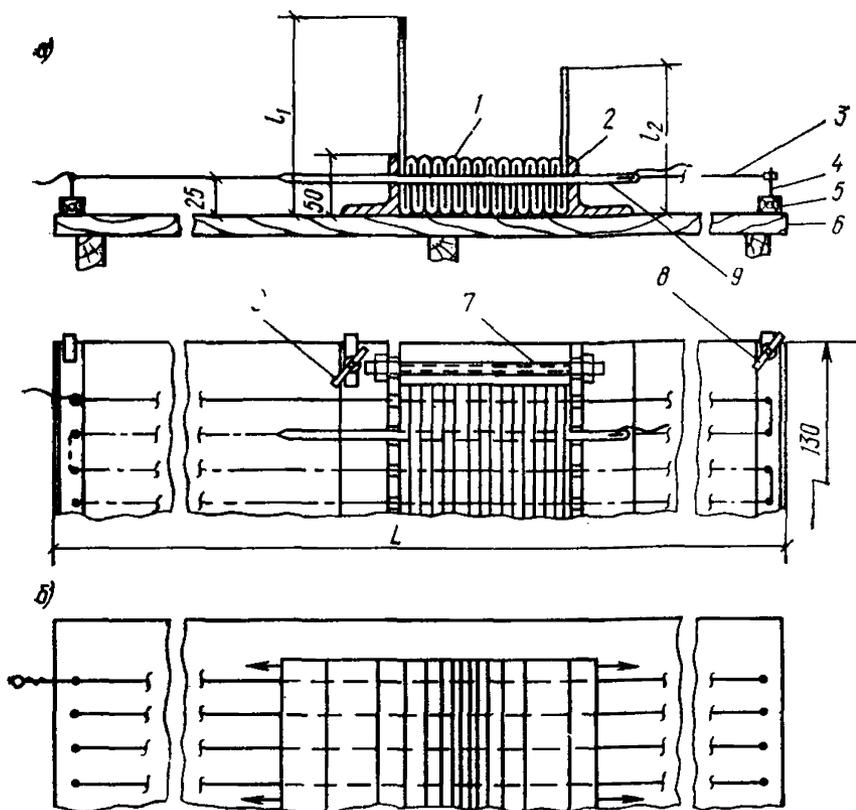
Схема изготовления нагревателя элемента ТАПП
